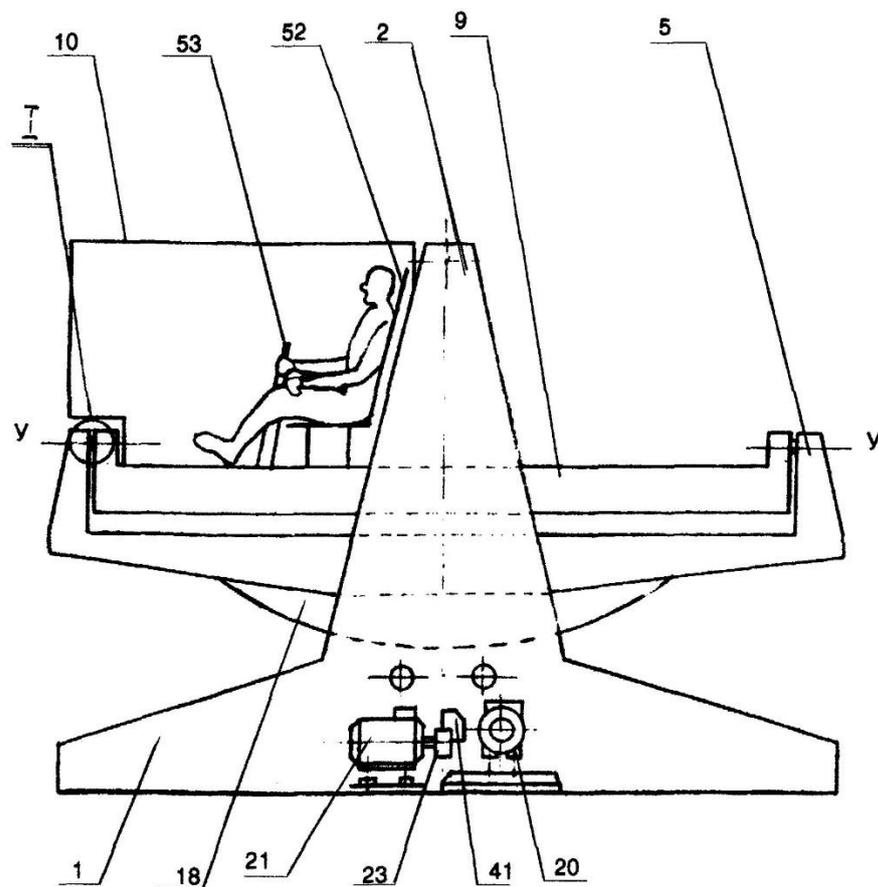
Общий вид конструкции [45]
